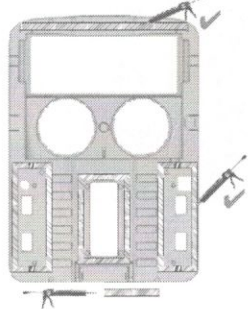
Sikaflex przy zakrzywieniu dachu przekraczającym 5200 mm albo przy dachu posiadającym rowki
